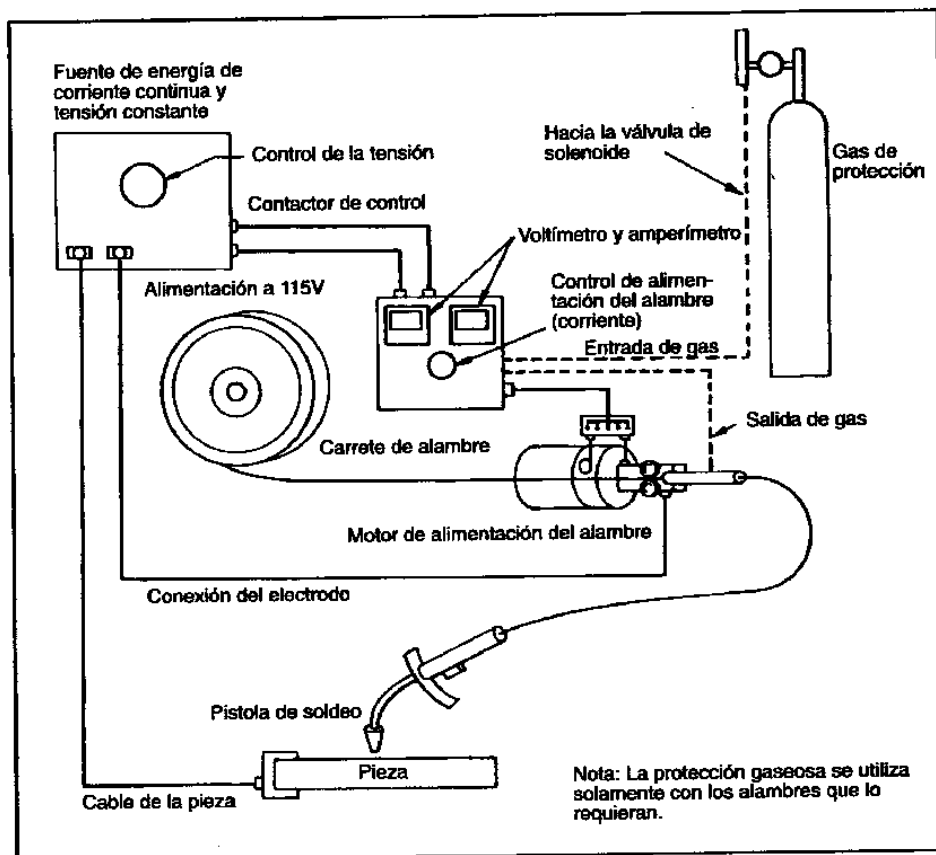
EQUIPO PARA EL SOLDEO POR ARCO CON ALAMBRE TUBULAR
